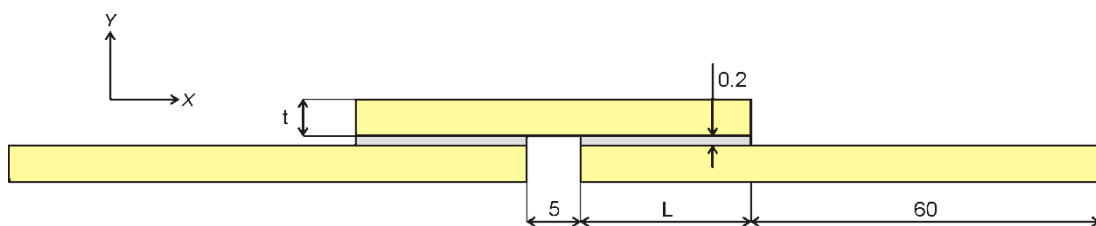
Geometria (mm) da junta de bissobreposição simples estudada.
